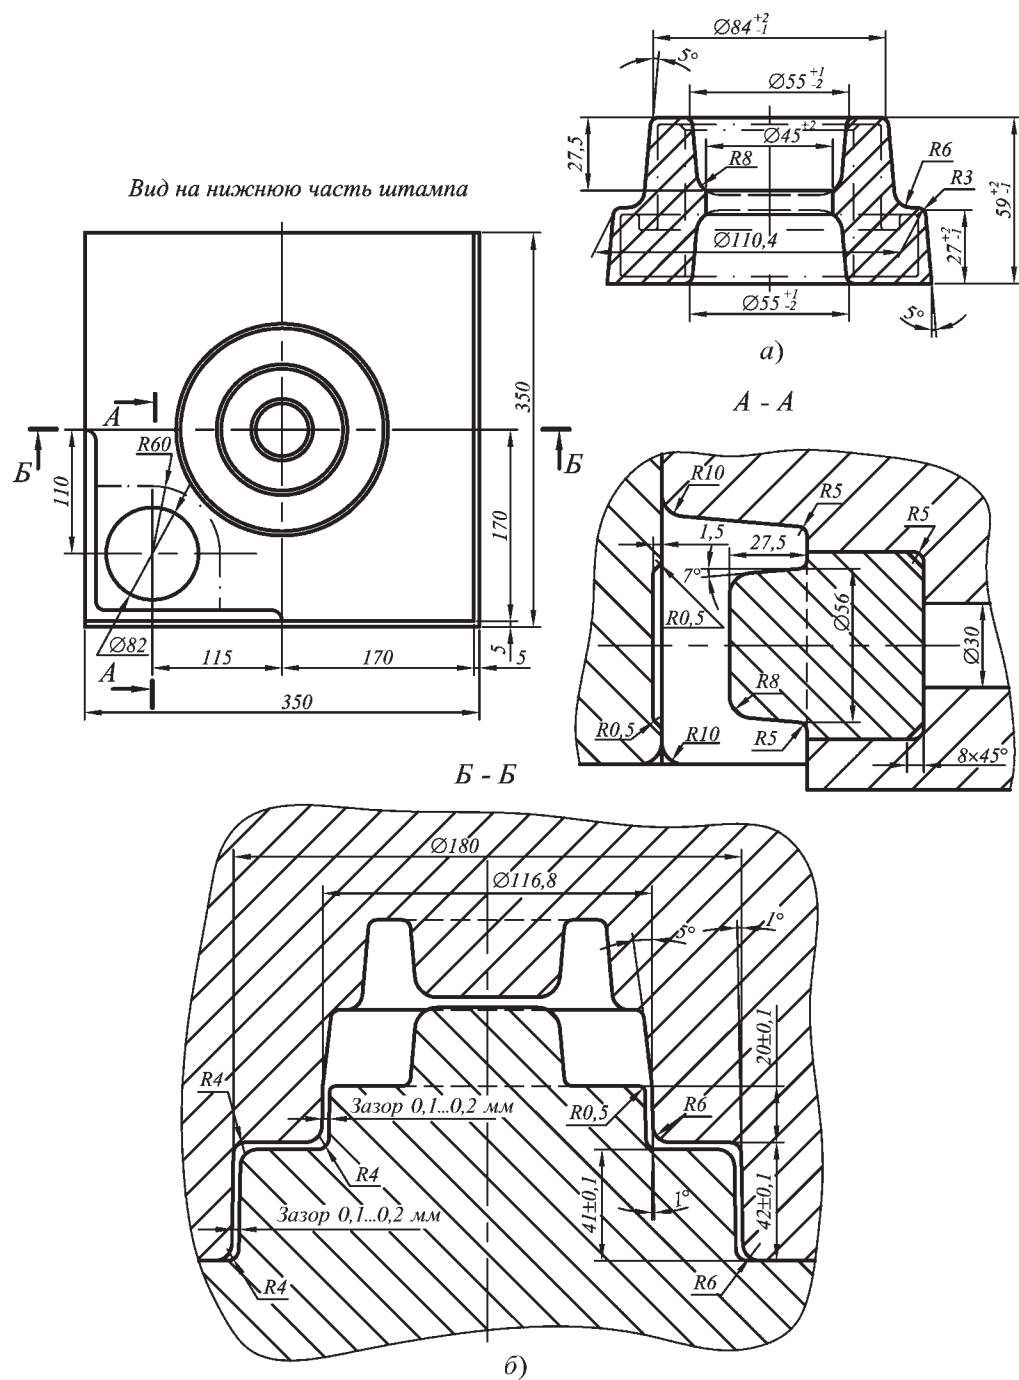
Чертеж поковки втулки (а) и закрытого молотового штампа (б)
